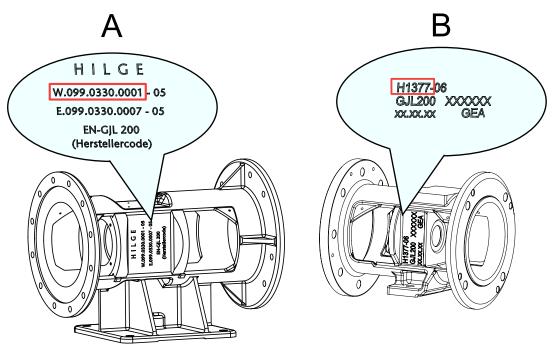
Существуют разные типоразмеры опор подшипников A - типоразмер 3 | В - типоразмеры 1 и 2
